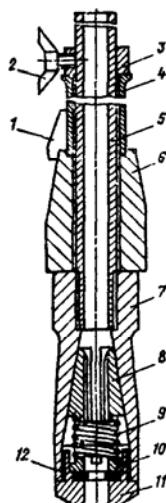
Приспособление для забивки заземлителей вручную:
